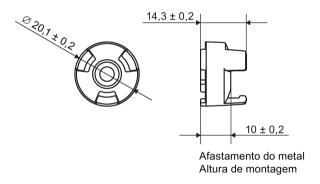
Desenho de dimensões do espaçador 6GT2690-0AG00
